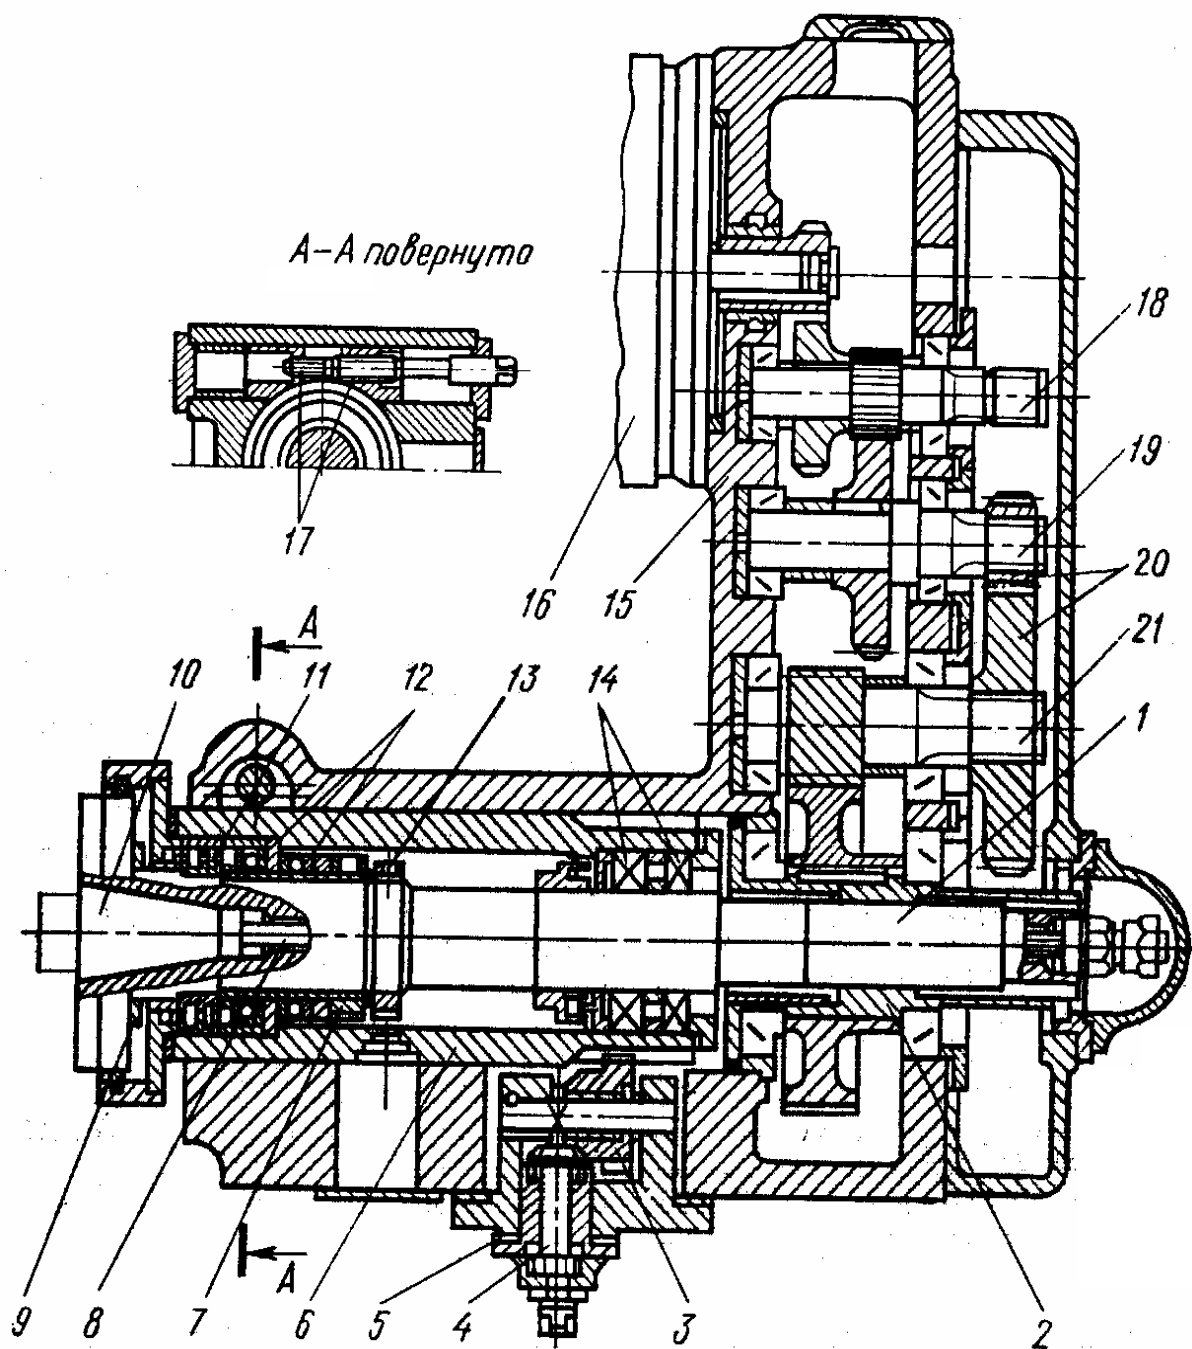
Фрезерна бабка: 1 - шпиндель; 2 - лицева втулка; 3 - конічне колесо-черв'як; 4 - рукоятка переміщення пінолі; 5, 9 - компенсатори; 6 - піноль-рейка; 7, 13 - гайки; 8 - шомпол; 10 - оправка; 11 - дворядний роликовий підшипник; 12 - упорні підшипники; 14 - радіально-упорні підшипники; 15 - корпус; 16 - електродвигун; 17 - сухарі фіксації пінолі; 18, 19, 21 - вали; 20 - змінне зубчасте колесо
